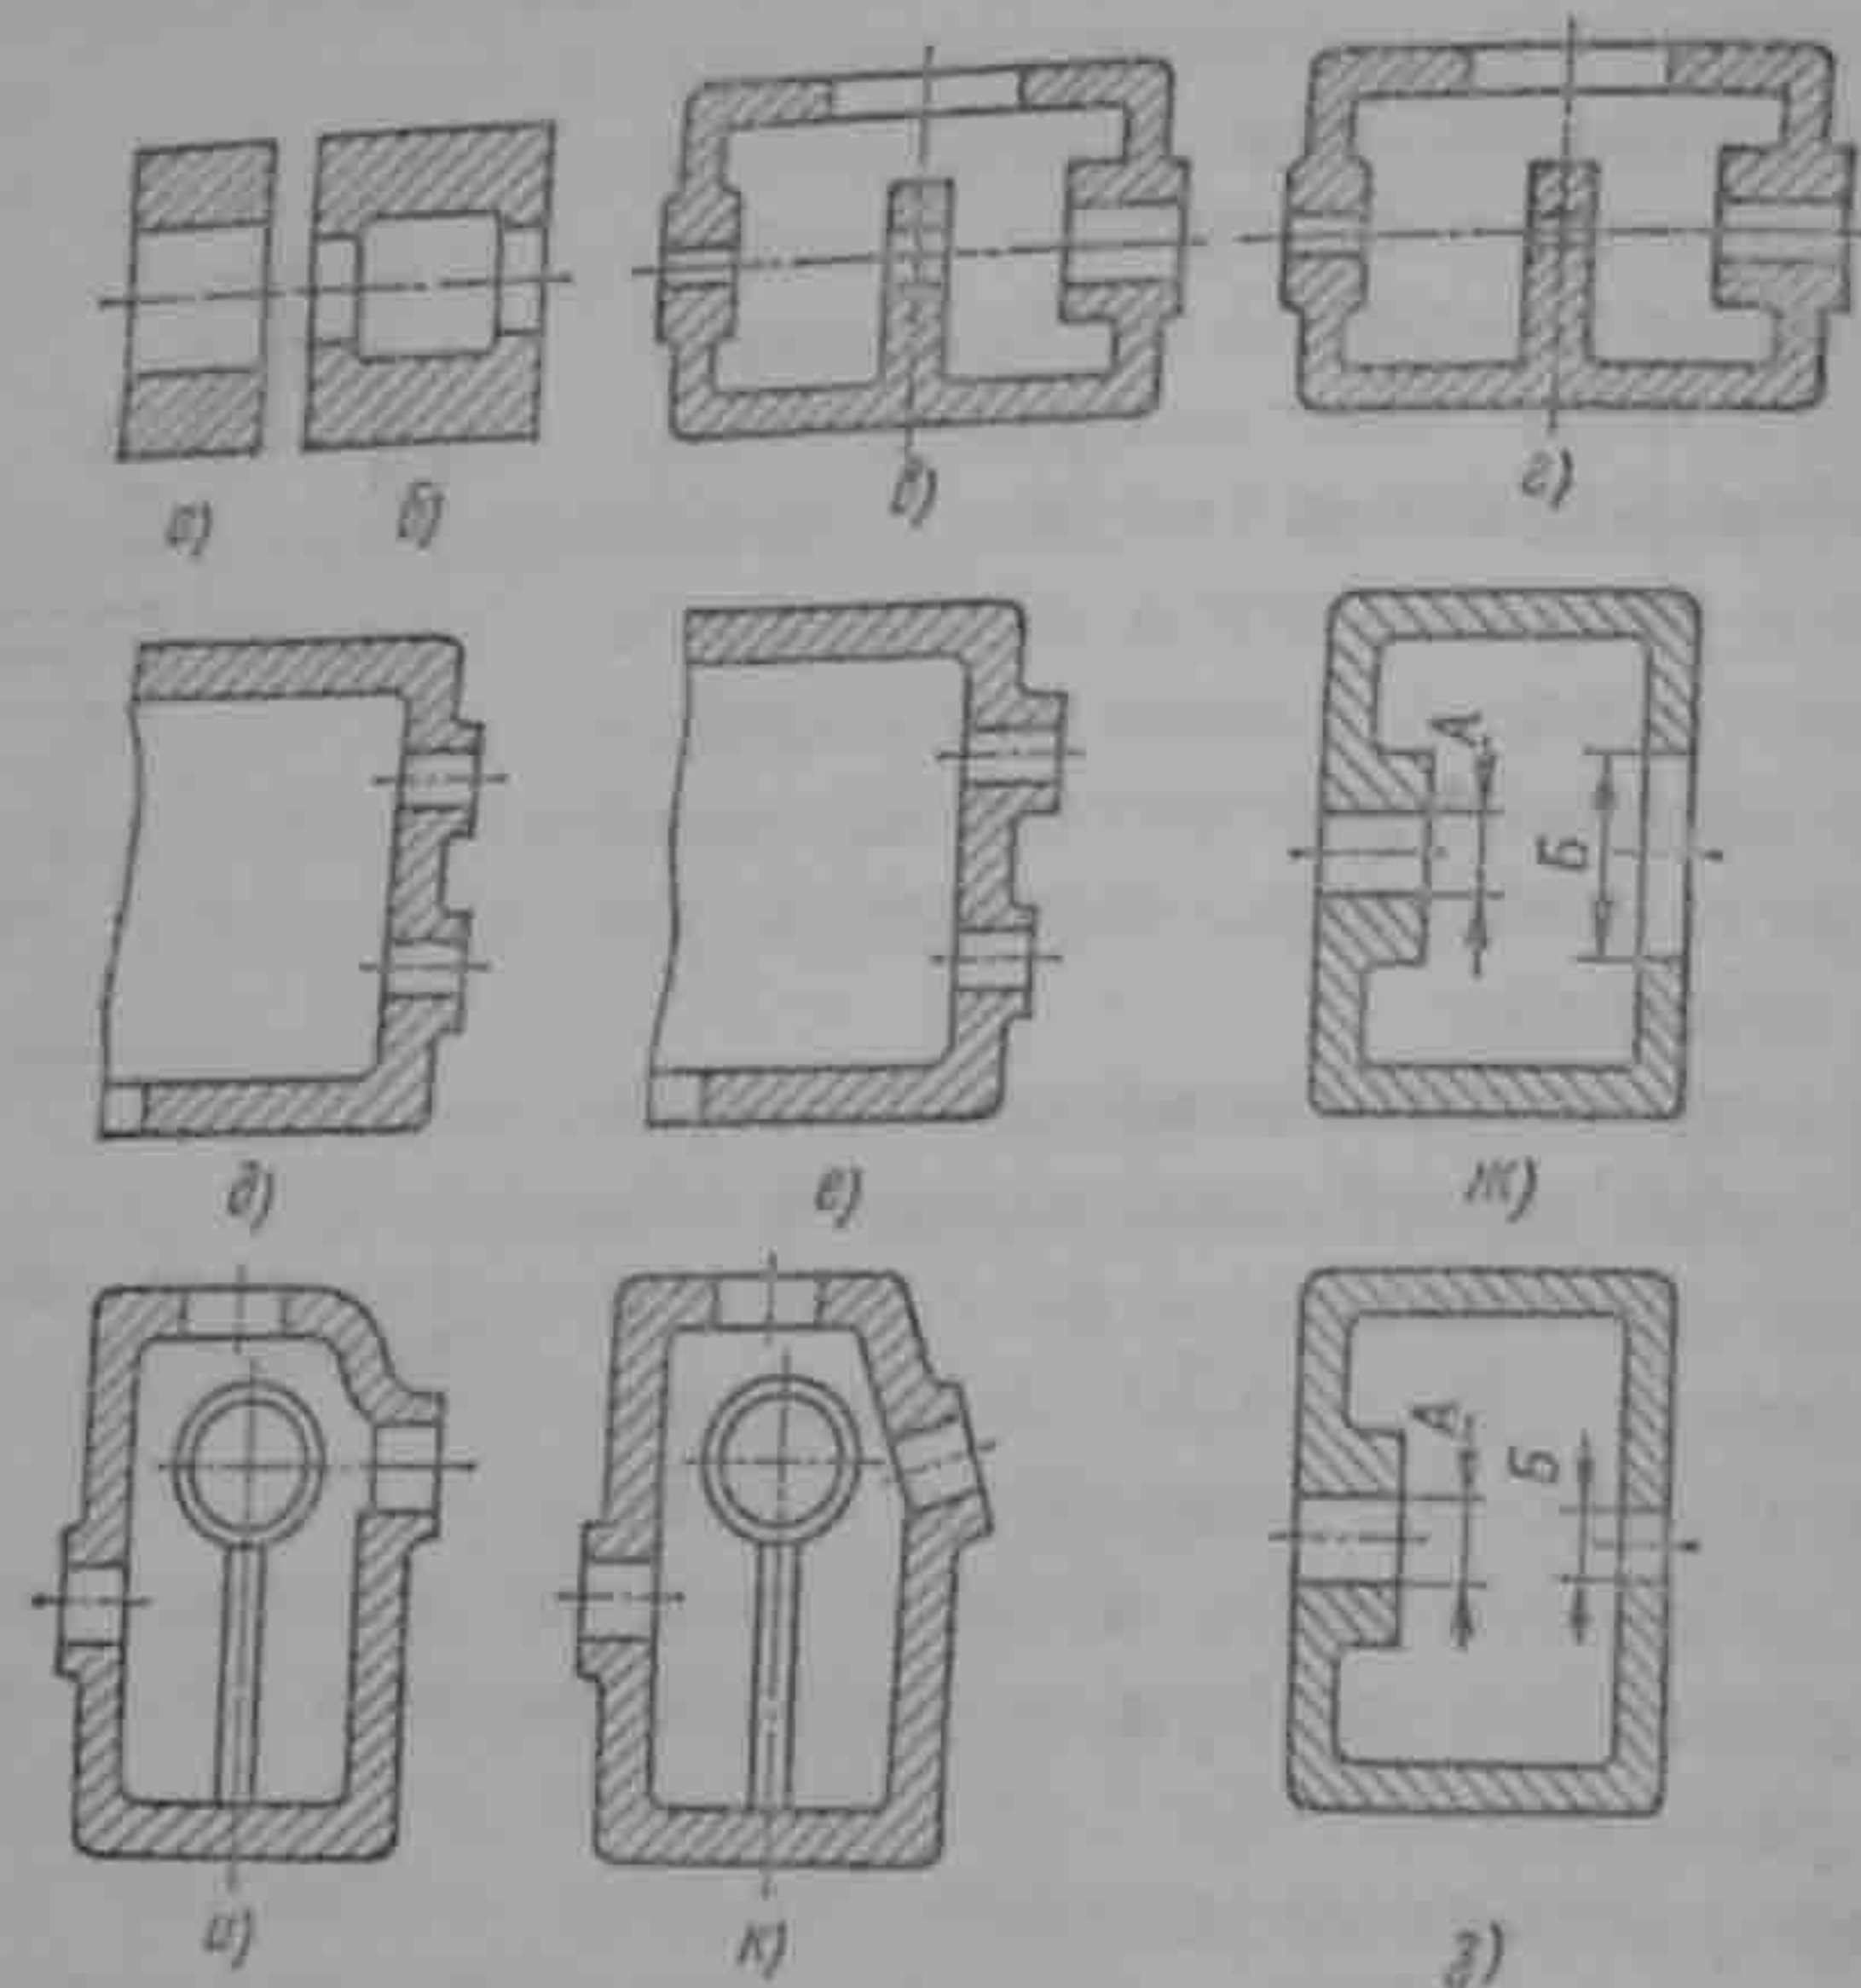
Примеры конструкций деталей машин, обрабатываемых на расточных станках
